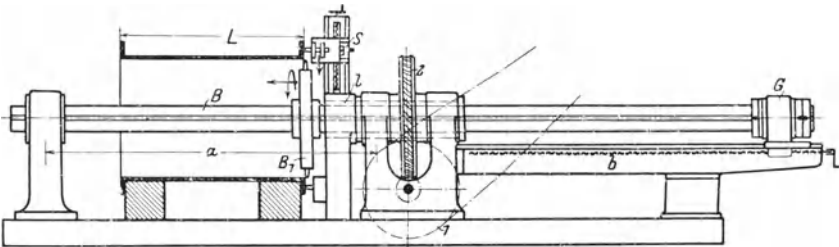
Zylinderbohrmaschine mit wandernder Bohrstange.
